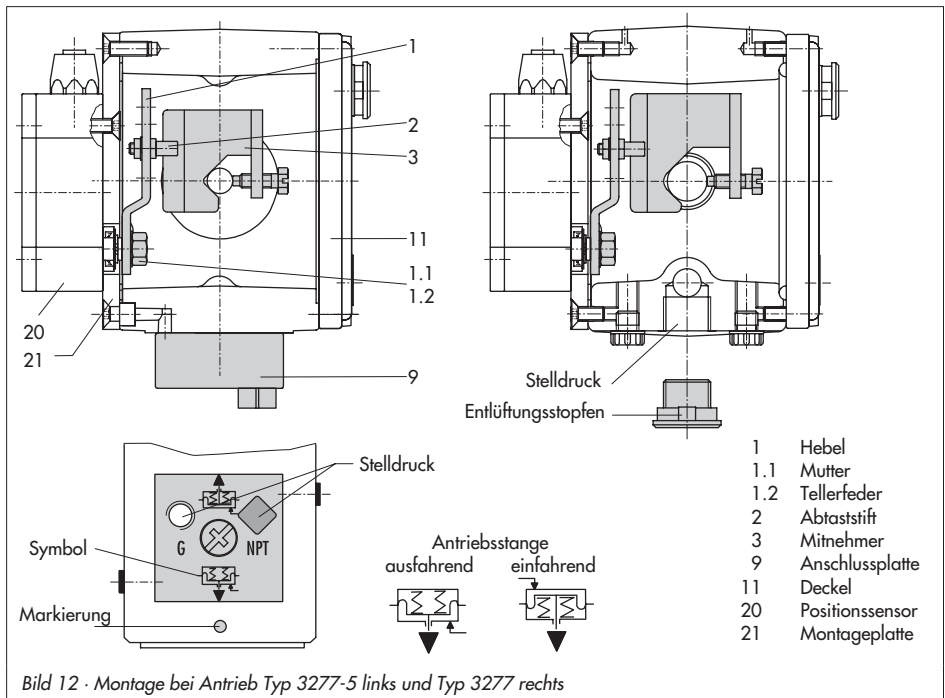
· Montage bei Antrieb Typ 3277-5 links und Typ 3277 rechts
